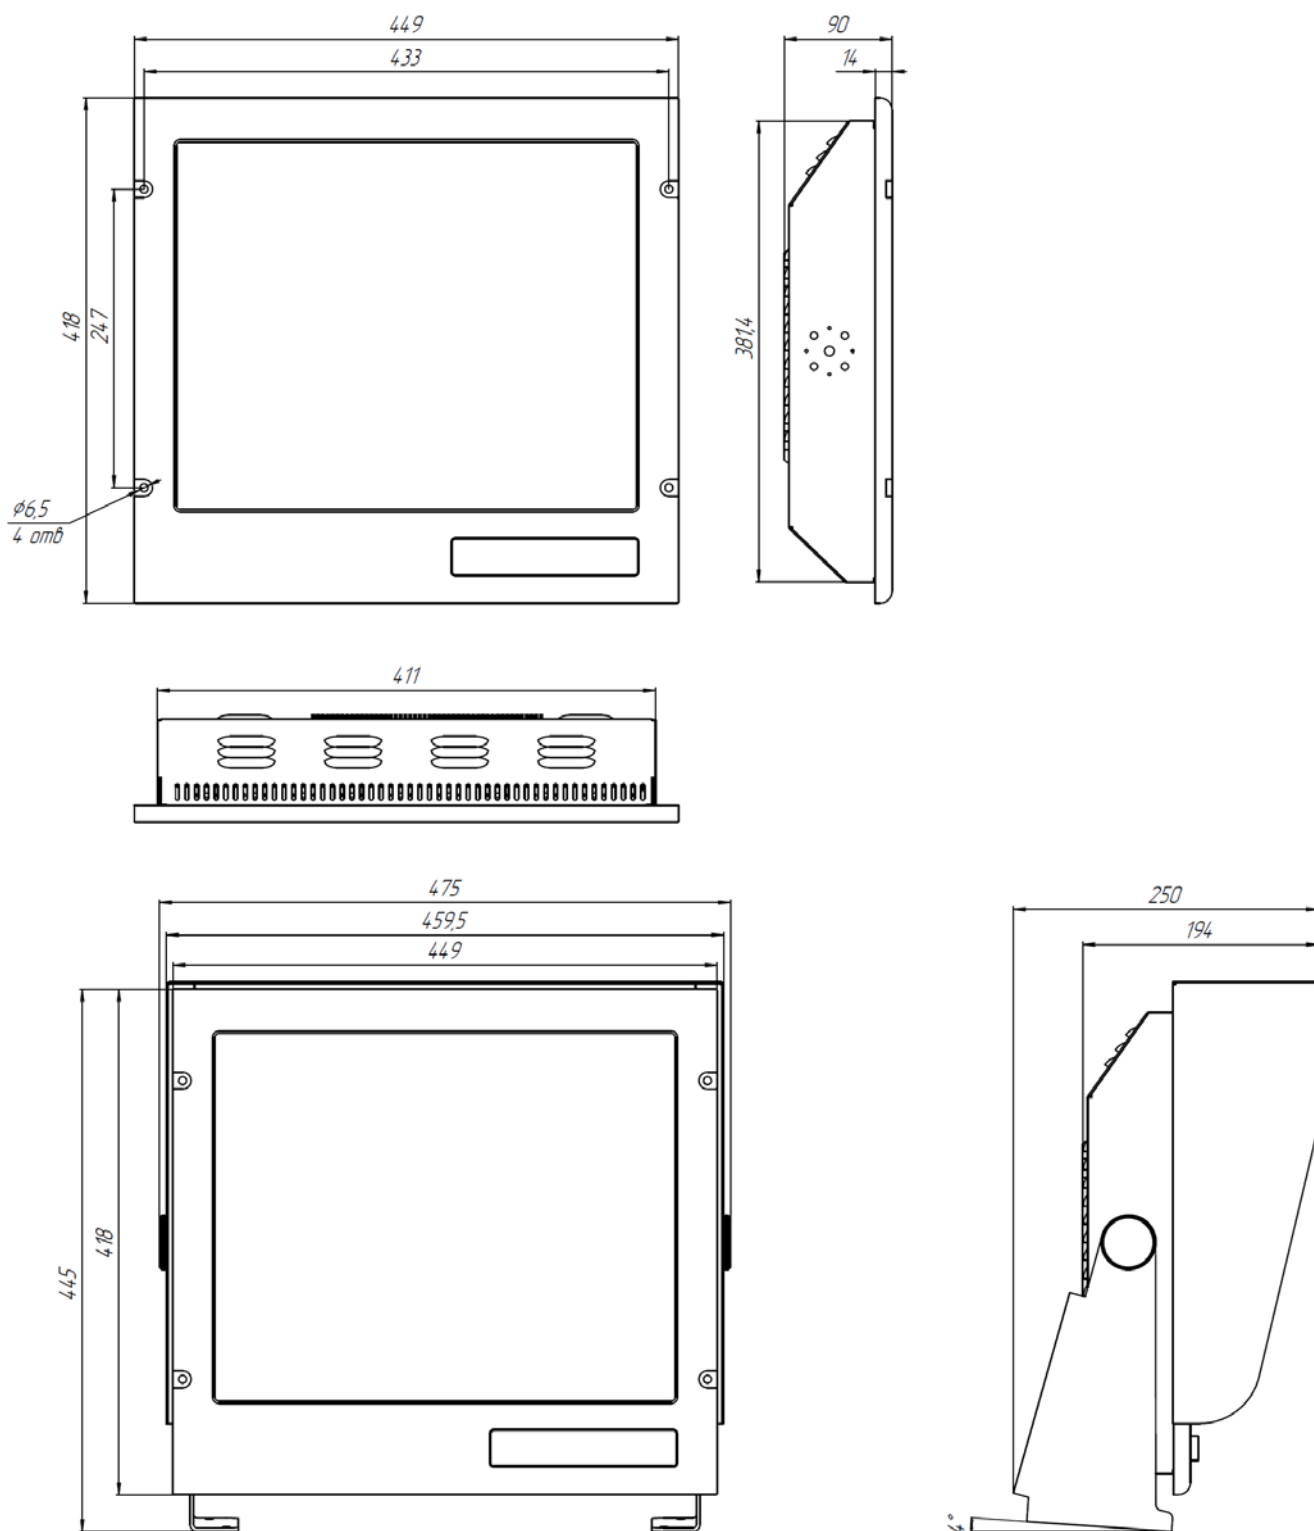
Габаритный чертеж (общий, на кронштейнах, с защитным козырьком)
